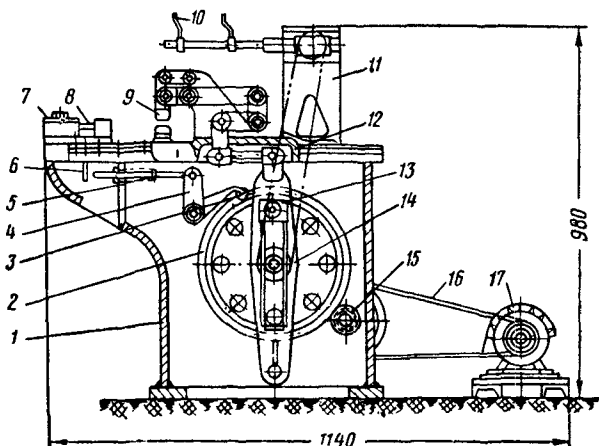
Станок-полуавтомат для калибровки текстолитовых клиньев:
